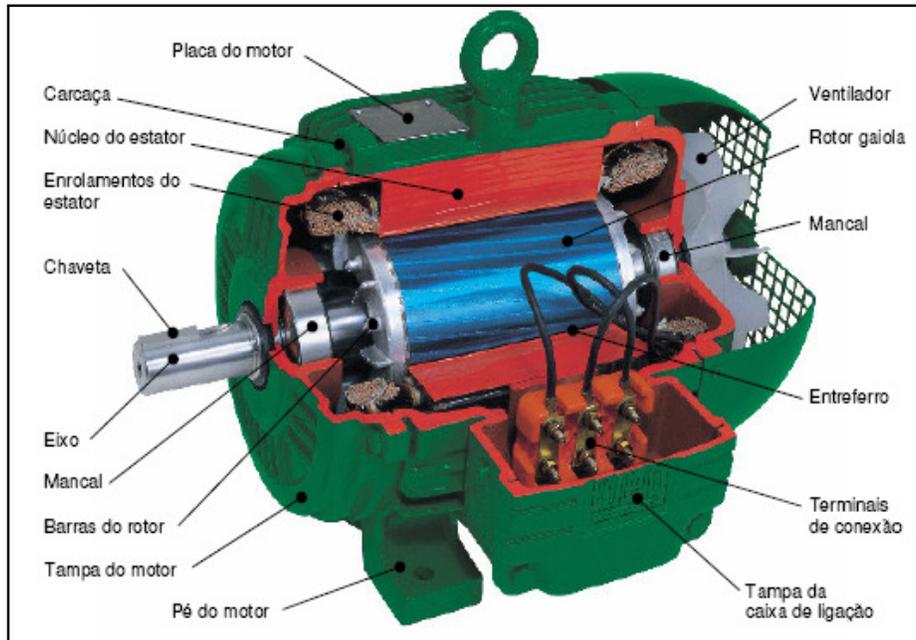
8: Corte de Motor Gaiola e seus componentes
